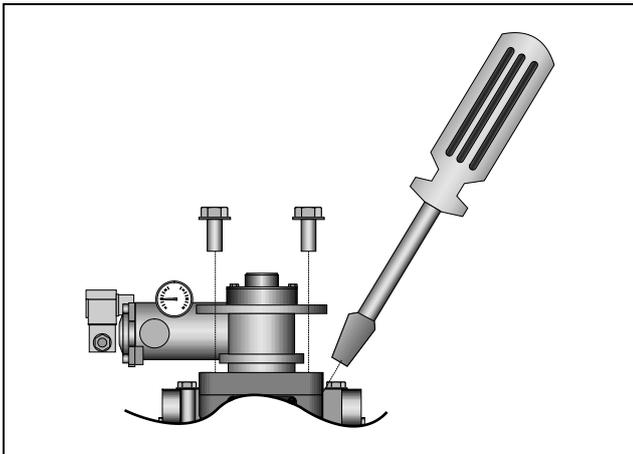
Desserrer et retirer les vis hexagonales du couvercle de filtre.
